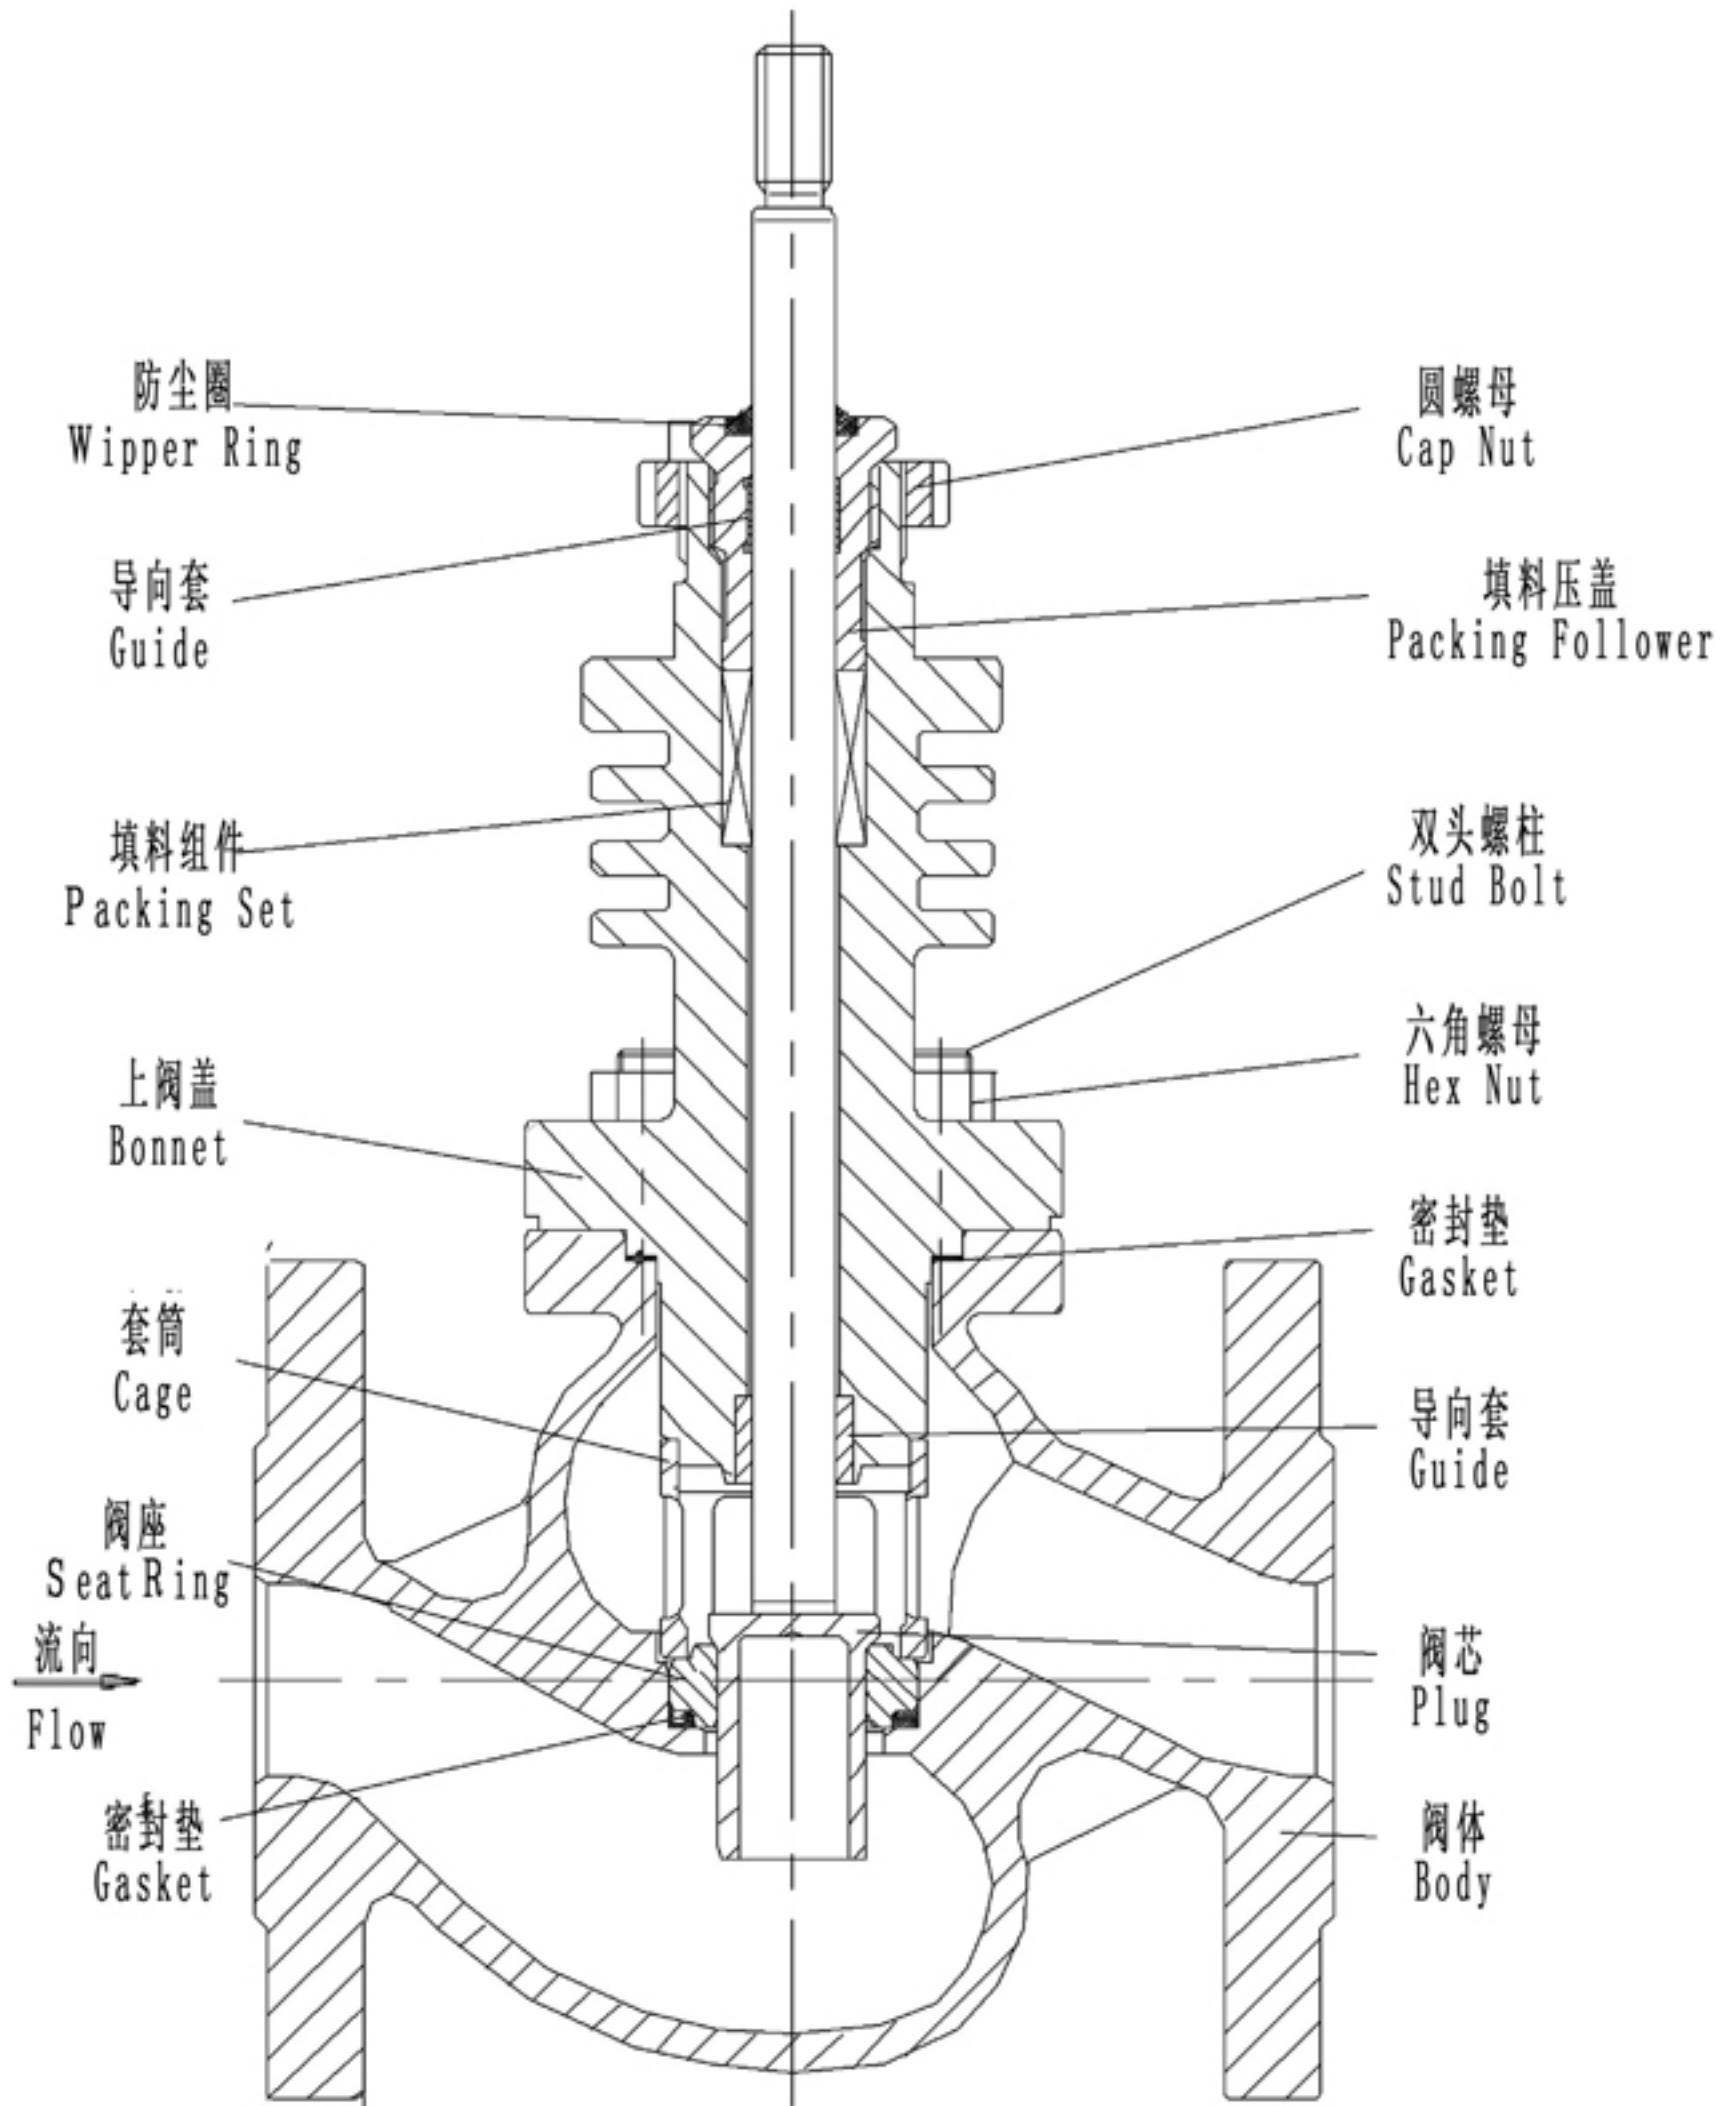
本体部构造 Fig.3 BODY SECTION VIEW
